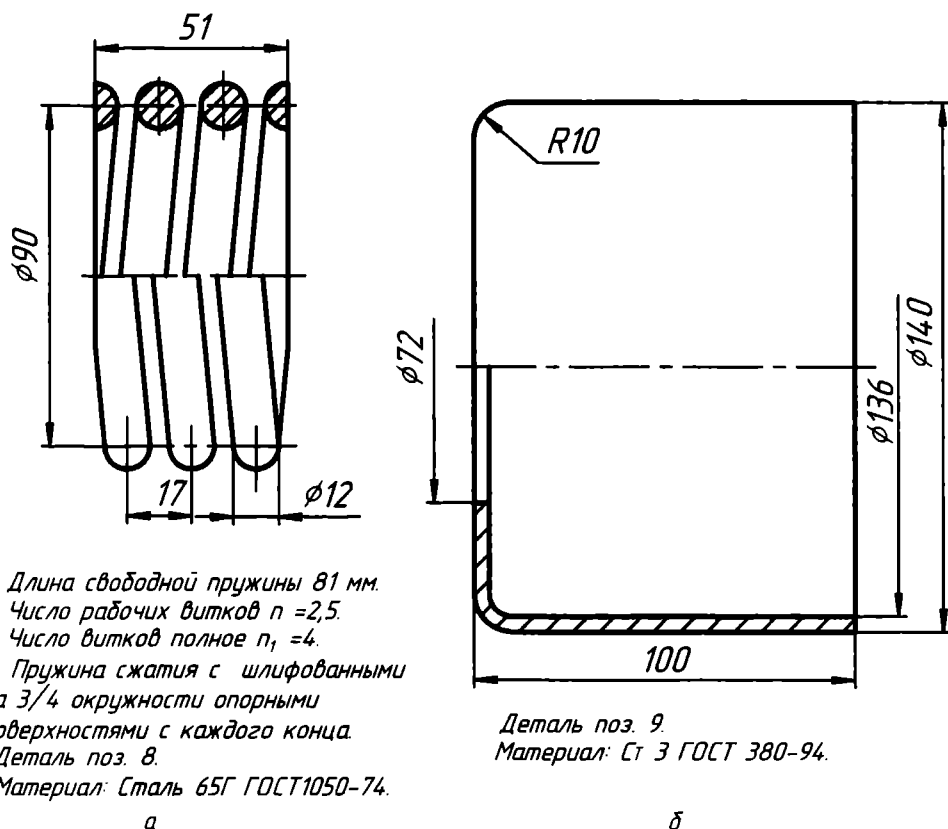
Чертежи: а — пружины; б — кожуха защитного
